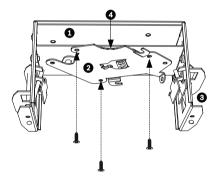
Fixar a placa de montagem ao suporte de montagem
